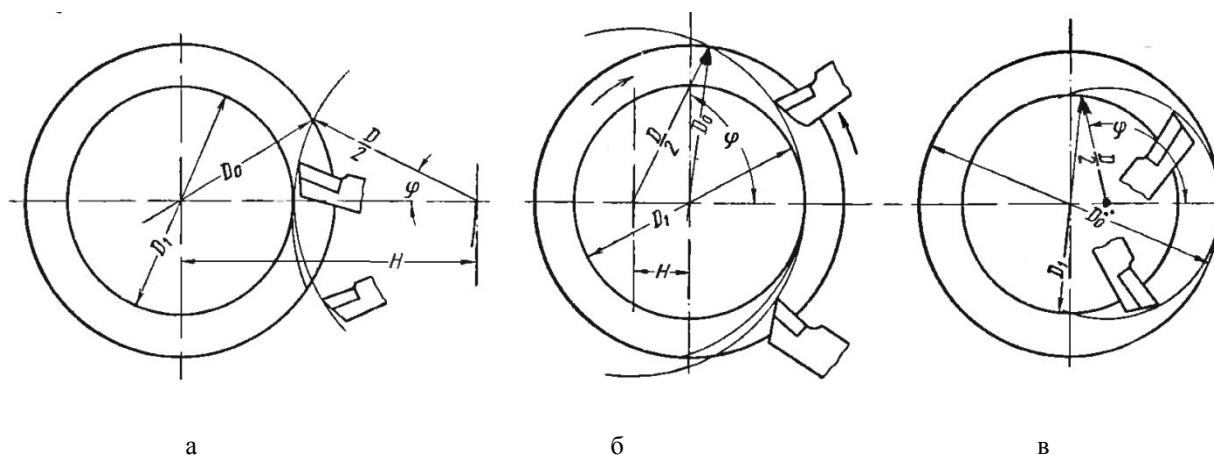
Вихревое нарезание резьбы. а - обработка наружной резьбы внешним касанием, б - обработка наружной резьбы внутренним касанием (охватывающее фрезерование), в - обработка внутренней резьбы внутренним касанием.
